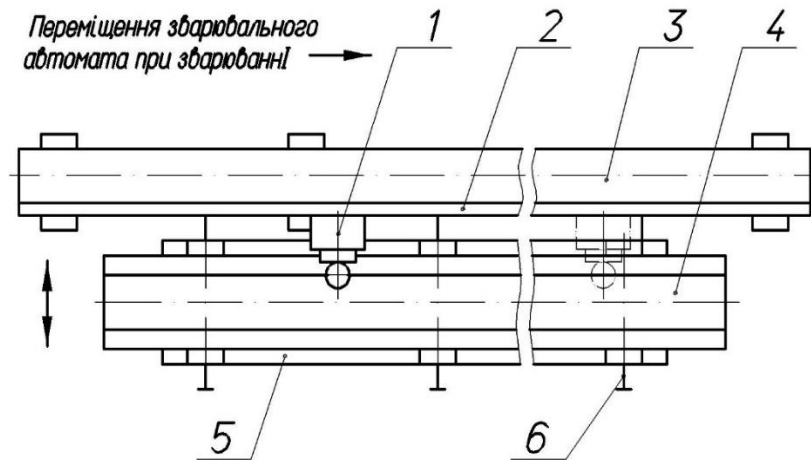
Схема зварювання балки при переміщенні автомата по напрямним стціонарного порталу зі швидкістю зварювання:
